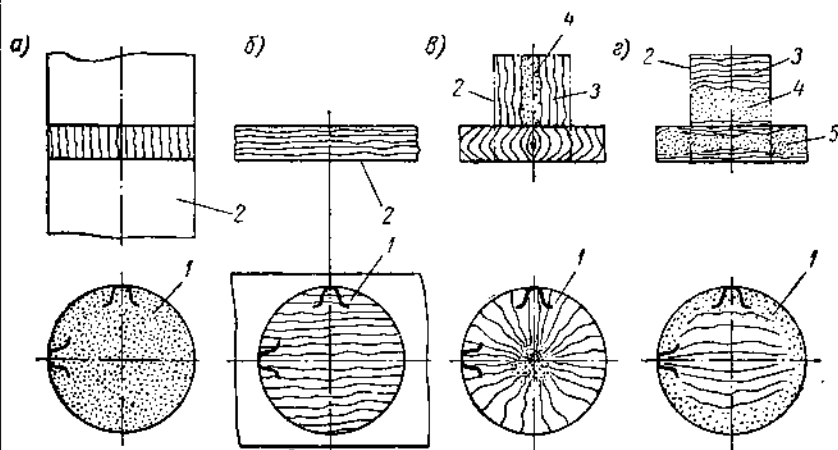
Изготовление шестерни 1 резанием из заготовки 2 с различным направлением макроволокна: а — из проката в виде прутка; б — из листового проката; в — из пруткового проката, подвергнутого предварительной осадке вдоль волокна; г — из проката, подвергнутого предварительной осадке поперек волокна;
